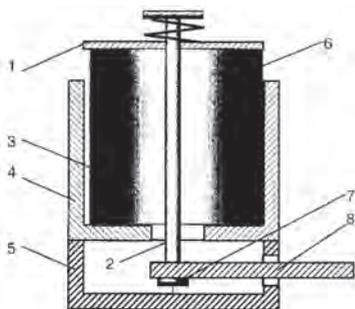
Конструктивная схема резинового виброизолятора подвешенного типа: 1–крышка; 2–стержень; 3–зазор; 4–кожух; 5–корпус; 6–резиновый упругий элемент; 7–головка стержня; 8–кронштейн для крепления к опорной поверхности станка.
